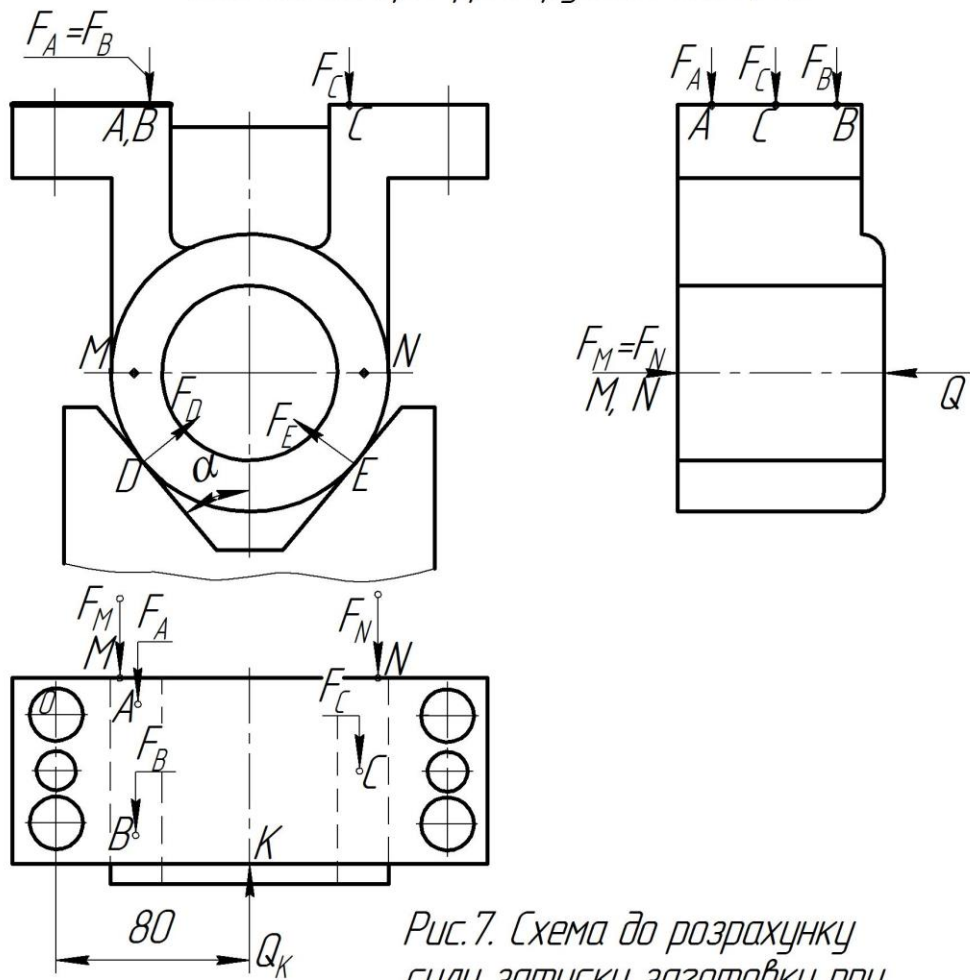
Схема до розрахунку сили затиску заготовки при свердлінні отворів
